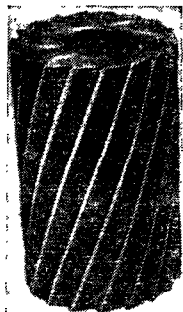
Основные конструктивные размеры цилиндрической фрезы
